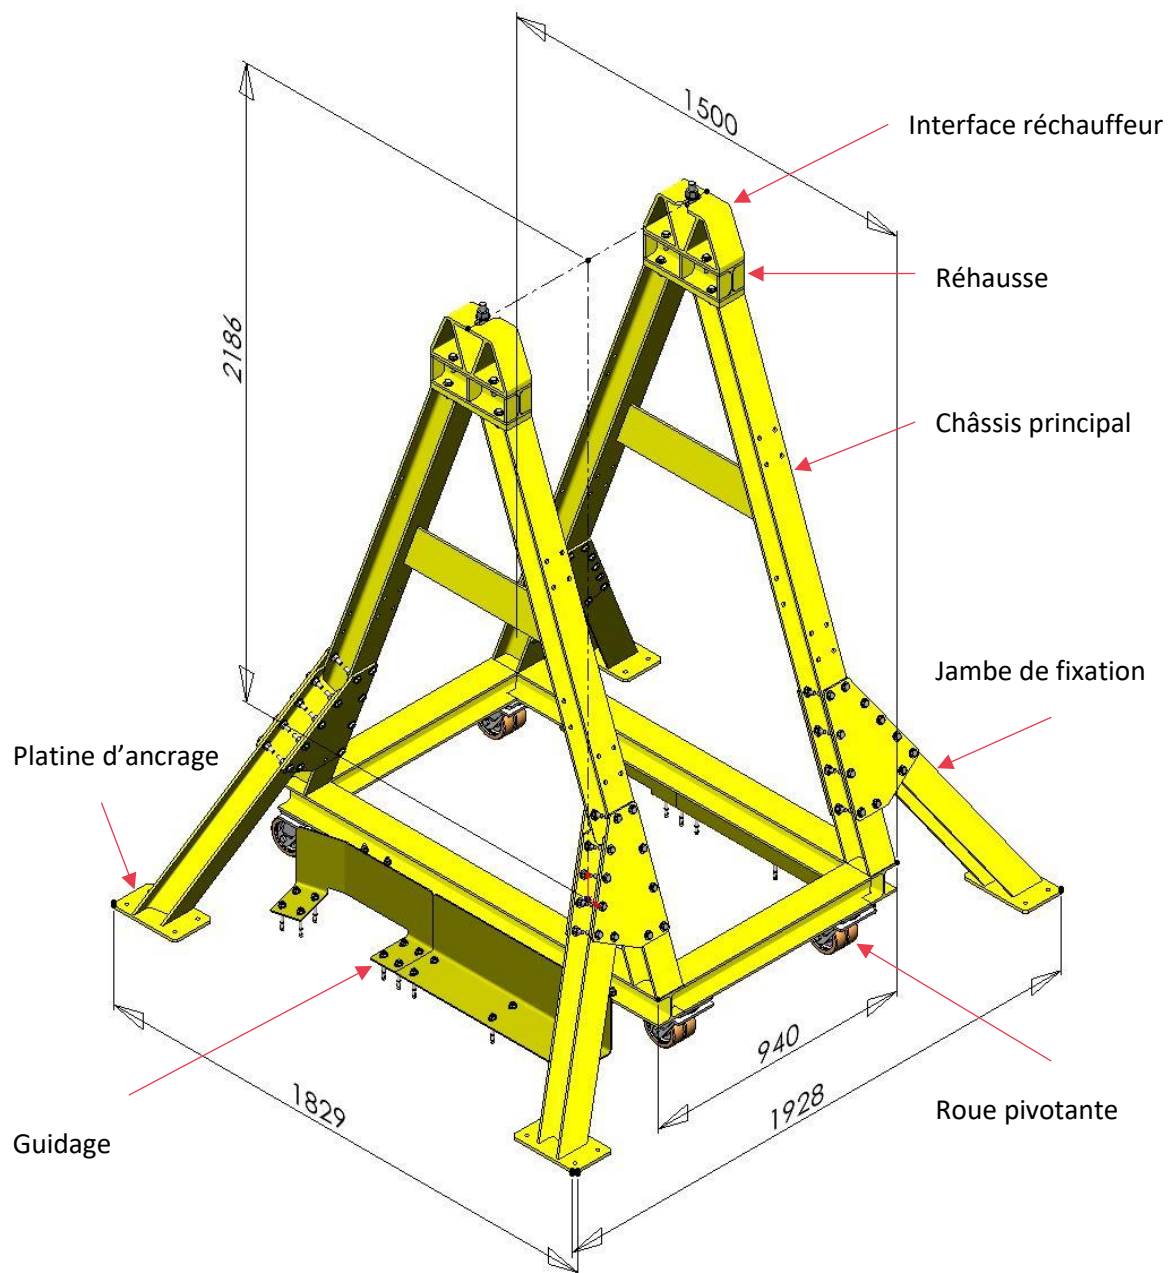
Vue isométrique du support réchauffeur ALCINA
